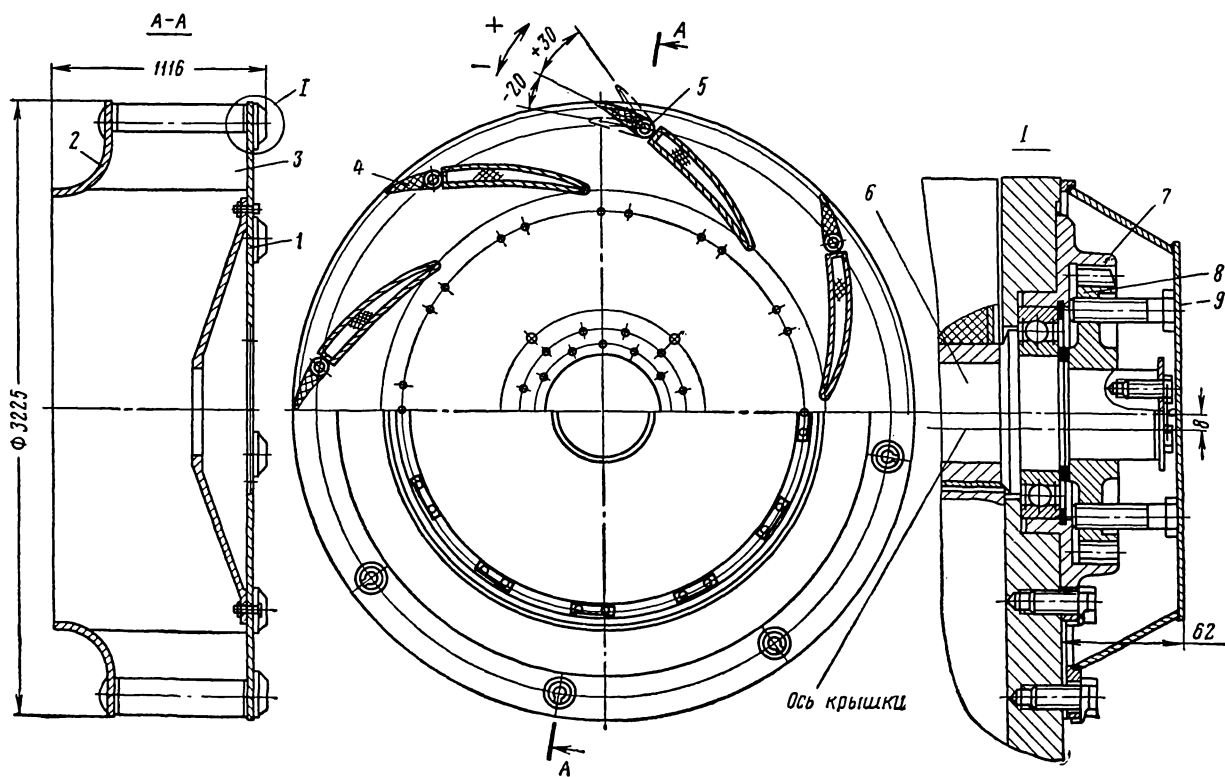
Рабочее колесо вентилятора ВЦЗ-32
